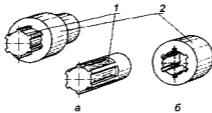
Шлицевое соединение (а) и его детали (б):
